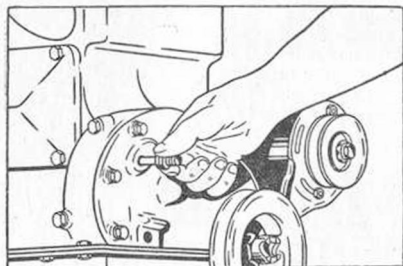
Определение положения коленчатого вала для установки момента зажигания
